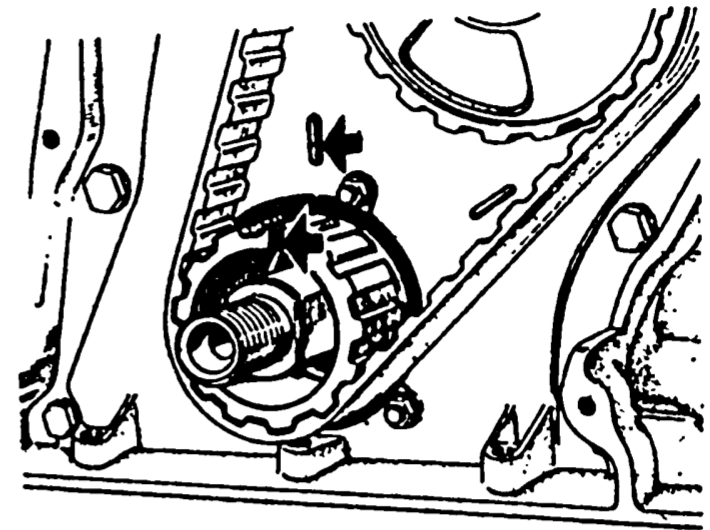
Проверка совпадения установочной метки на шкиве коленчатого вала с меткой на крышке привода распределительного вала
